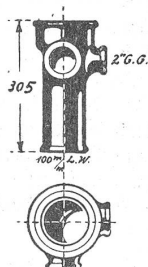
mit zwei 2" Gewindeanschlüssen
